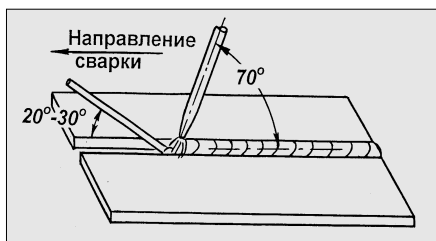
Сварка тонких листов с подачей присадочного металла в дугу
